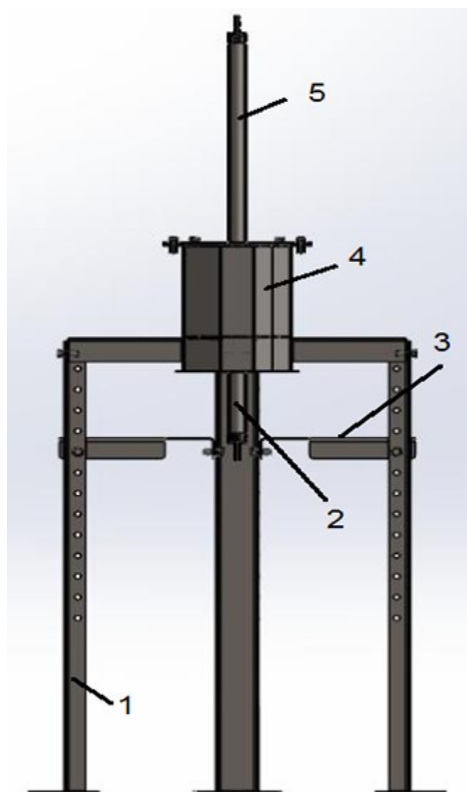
Реактор для збагачення синтезгазу: 1– опорна лапка; 2 – вхідний патрубок; 3 – полка для пальника; 4 – робоча камера; 5 – Вихідний патрубок.
